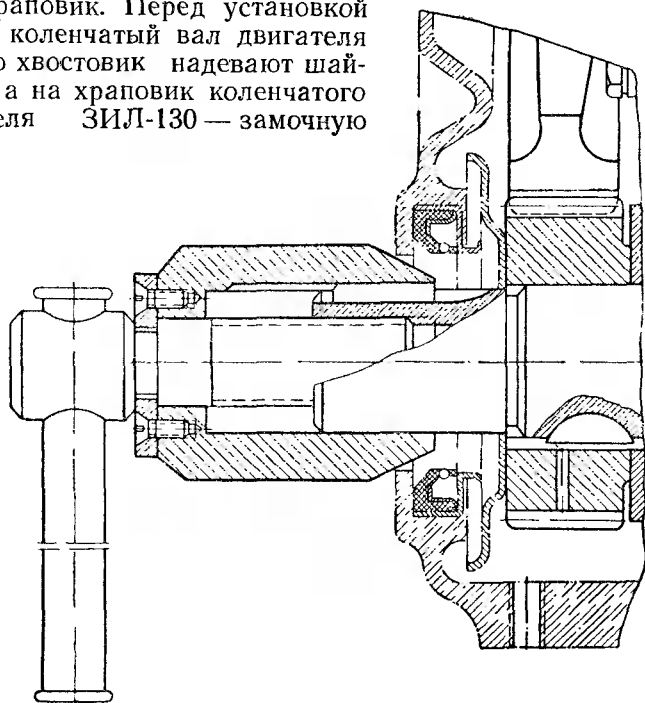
Оправка для центрирования крышки распределительных шестерен
